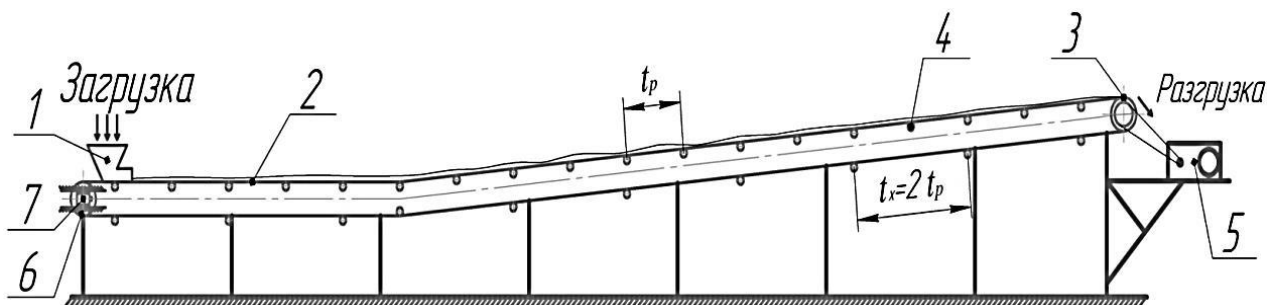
Схема ленточного конвейера: 1 – загрузочное устройство; 2 – конвейерная лента; 3 – приводной барабан; 4 – опорный ролик; 5 – привод; 6 – натяжной барабан; 7 – натяжное устройство
